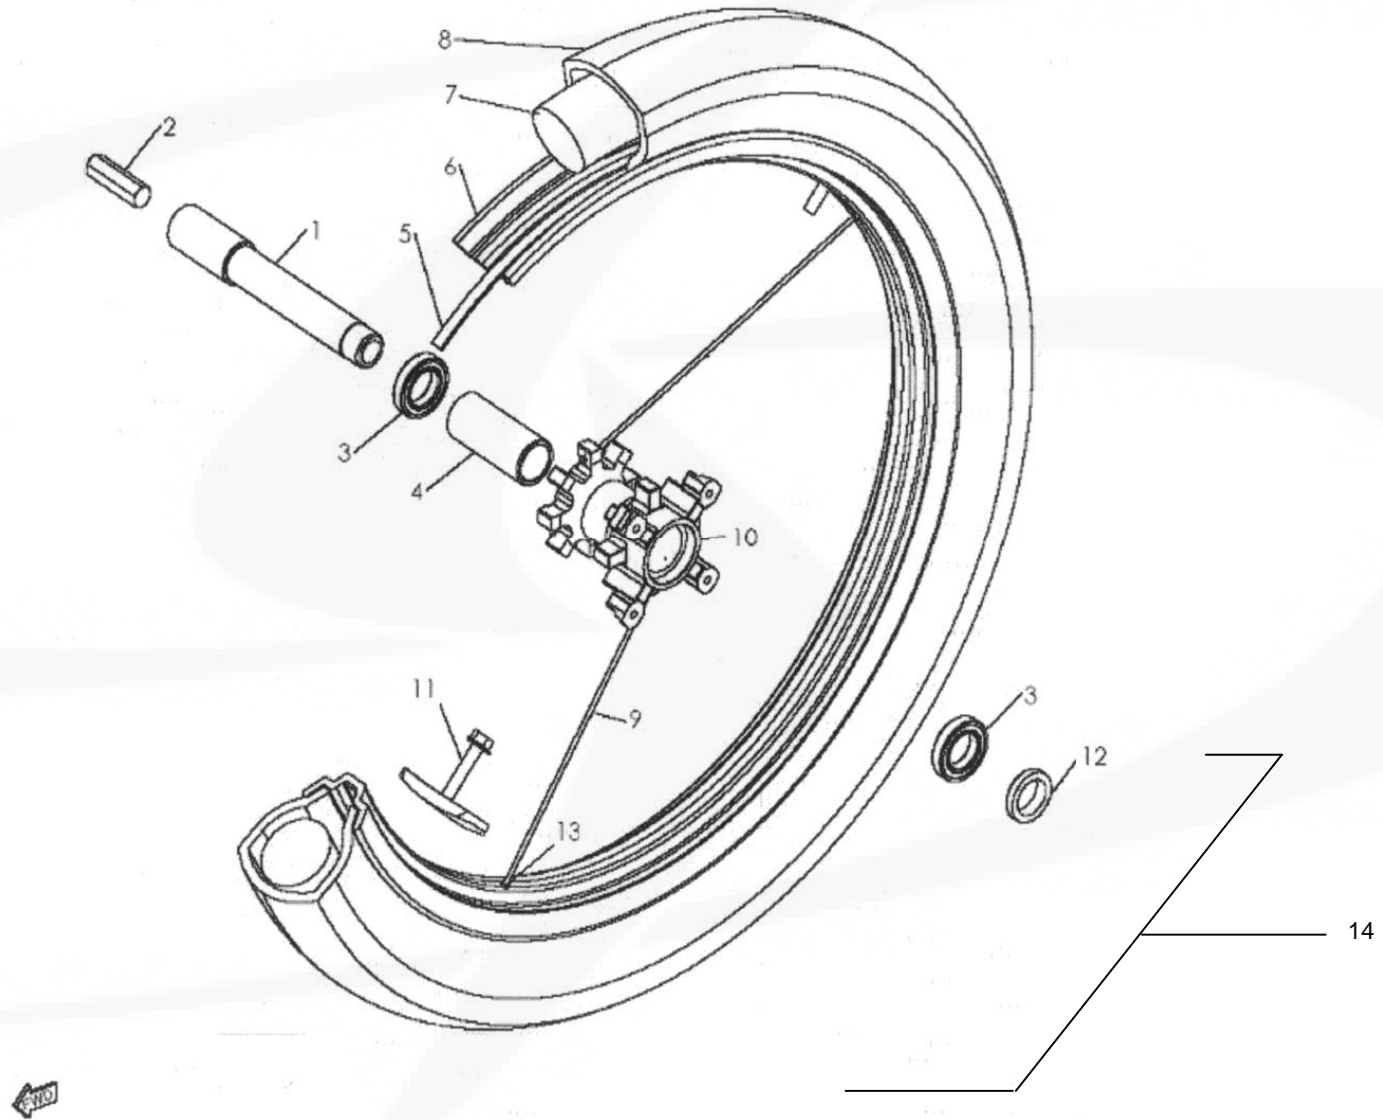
ROUE AVANT / FRONT WHEEL / RUEDA DELANTERA
